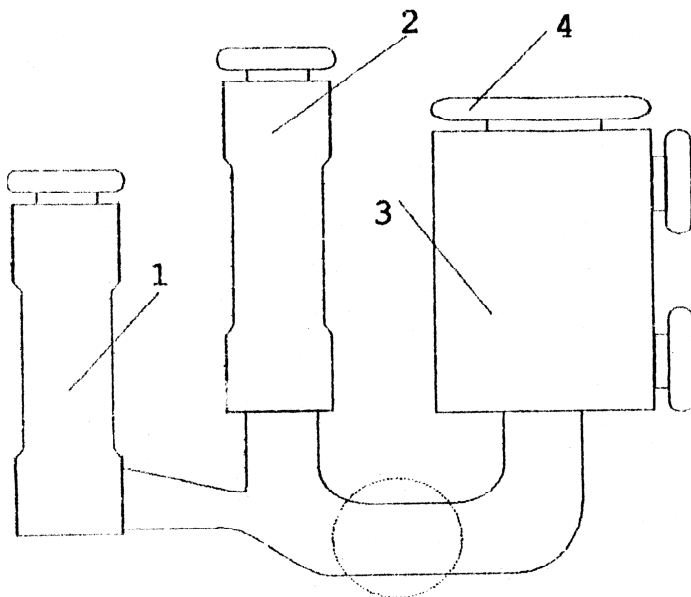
Схема питания отливок и вентиляции пресс-формы:
